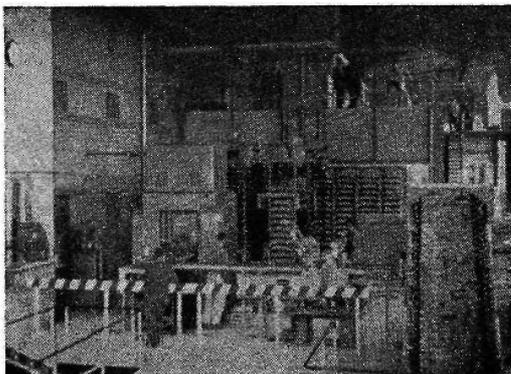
Una vista del conjunto de la prensa, máquina de puente móvil, y, en el fondo, entrada al secadero de doble galería.
